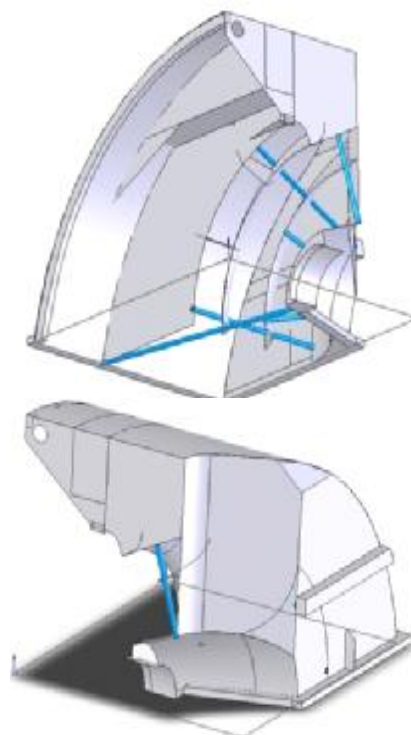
Четвертина кришки корпусу турбіни К-500 (вихідна конструкція)
